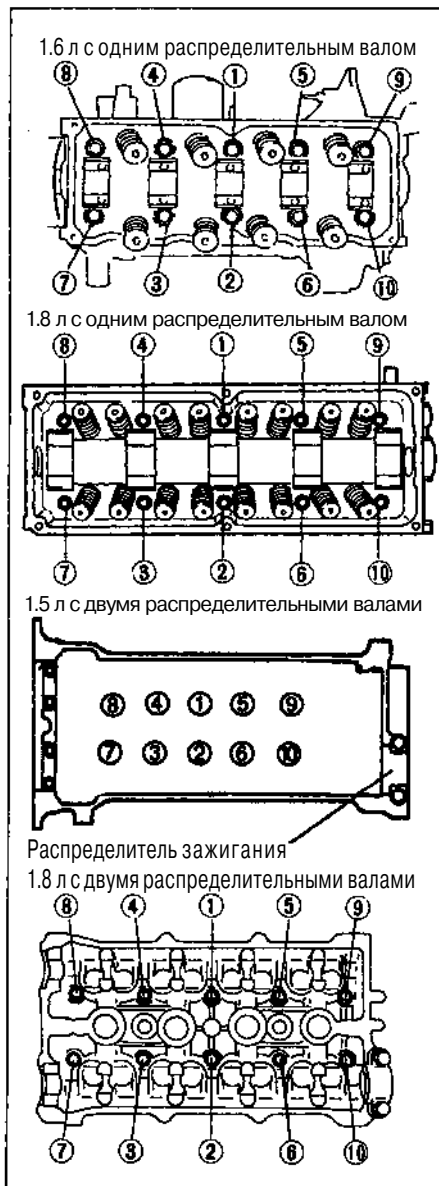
Порядок ЗАТЯЖКИ болтов головки цилиндров
